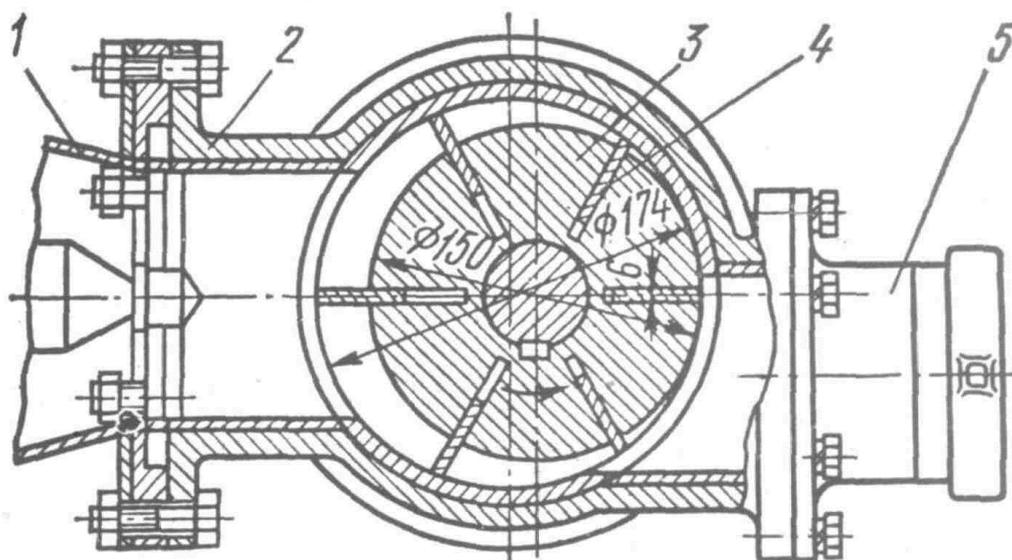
Роторный шиберный насос: 1 – всасывающий патрубок; 2 – корпус насоса; 3 – ротор; 4 – шиберные пластины; 5 – нагнетательный
